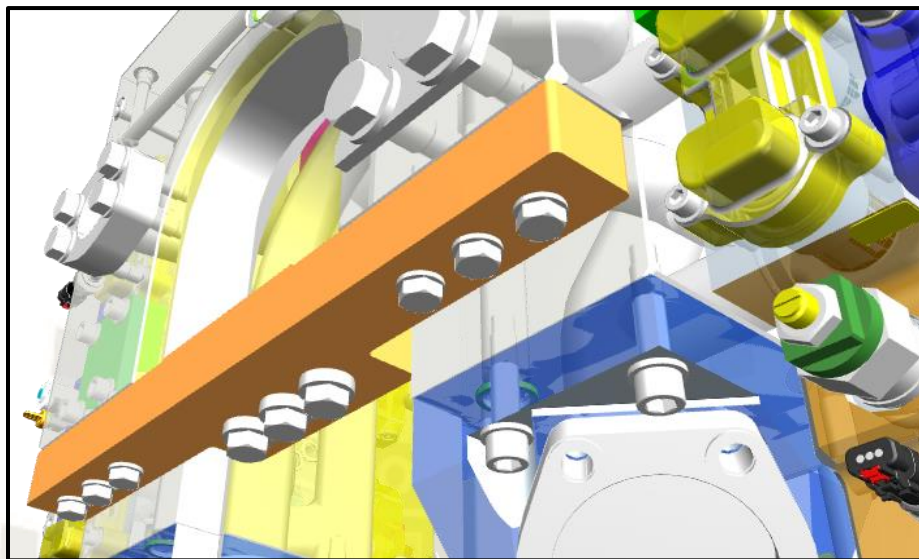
Diseño de placa de montaje mejorada (Mounting Plate)
